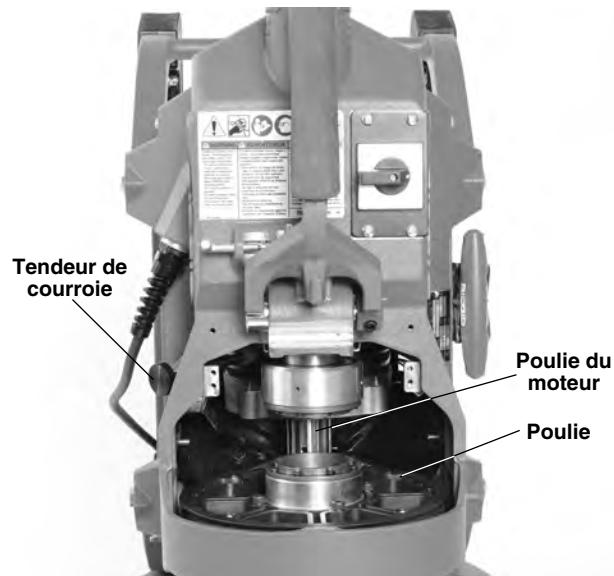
Machine debout sur sa face arrière avec tiroir à copeaux enlevé
